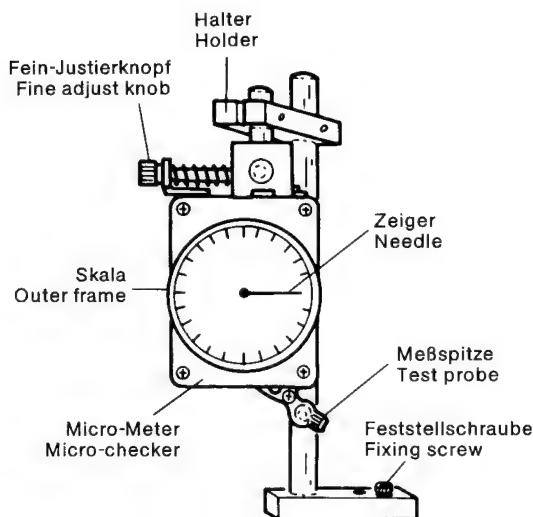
Mikrolehre / Micro-checker
